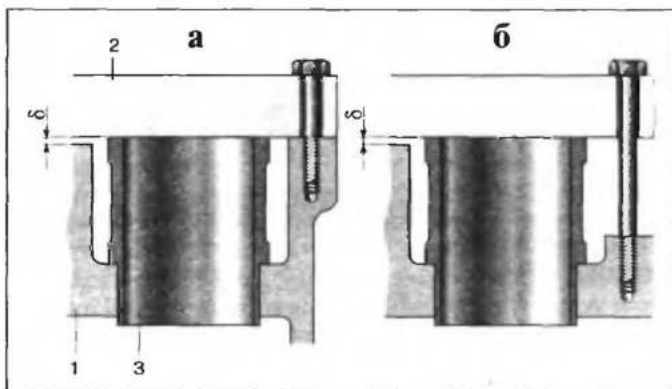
Схема установки болтов крепления головки блока с "мокрыми" гильзами:
